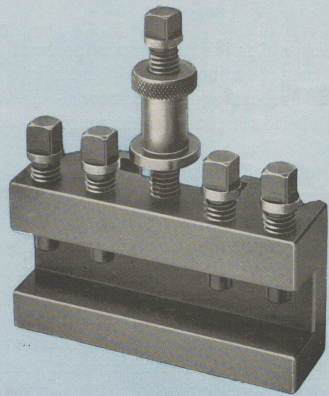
Werkzeughalter mit rechteckigem Querschnitt für Schruppstähle, Seitenstähle, Abstechstähle usw.
